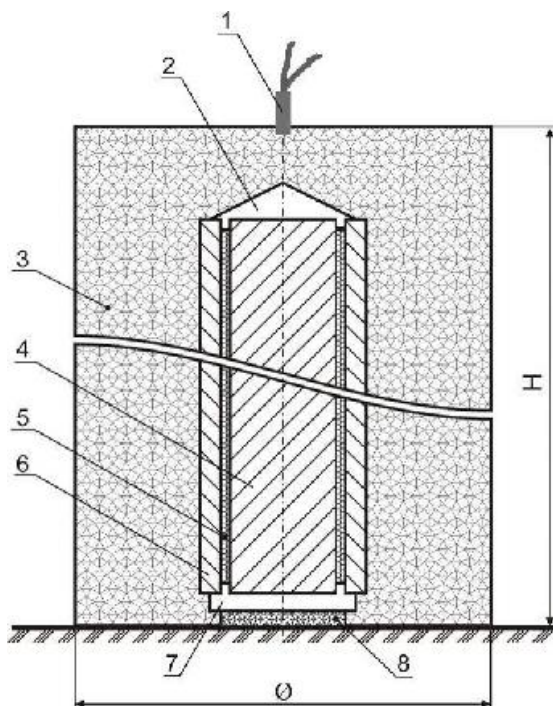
Схема прессования взрывом порошка между трубой и цилиндром наружным зарядом ВВ: 1 – детонатор; 2 – заглушка верхняя; 3 – заряд ВВ; 4 – цилиндр; 5 – прессуемый порошок; 6 – труба; 7 – заглушка нижняя; 8 – подставка; ($H \approx 3 \div 4 \text{ } \varnothing$)
